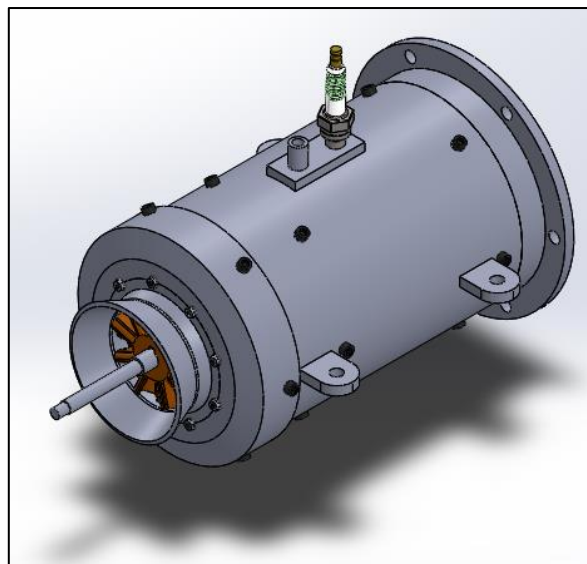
Vista isométrica modelo CAD turbina a gas diseño final – SolidWorks 2014 (elaboración propia)
